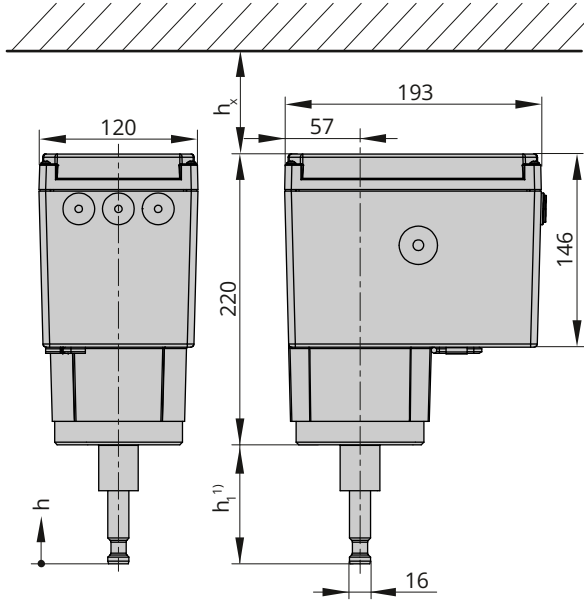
mm cinsinden boyutlar · Tip 3374-15, -17, -26 ve -36 (form A)
